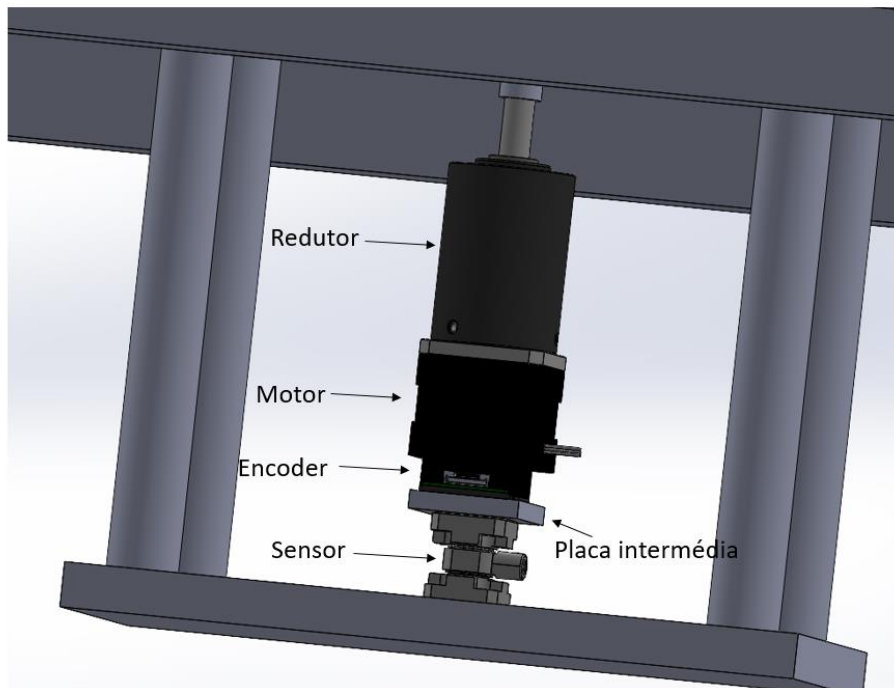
Pormenor do conjunto redutor/motor/encoder/sensor/placa intermédia.
